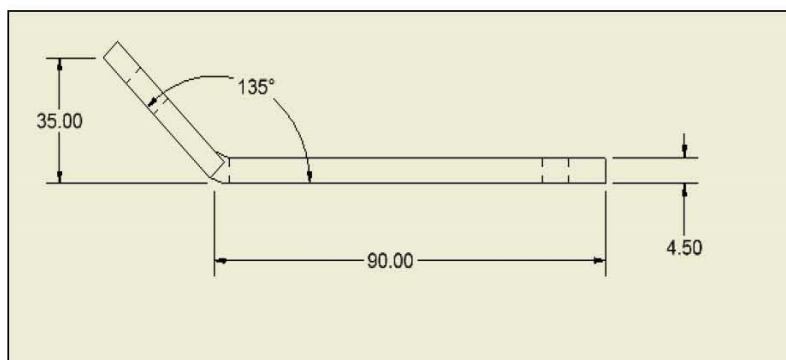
Montage lumière stroboscopique dimensions du support pour KX080-3
